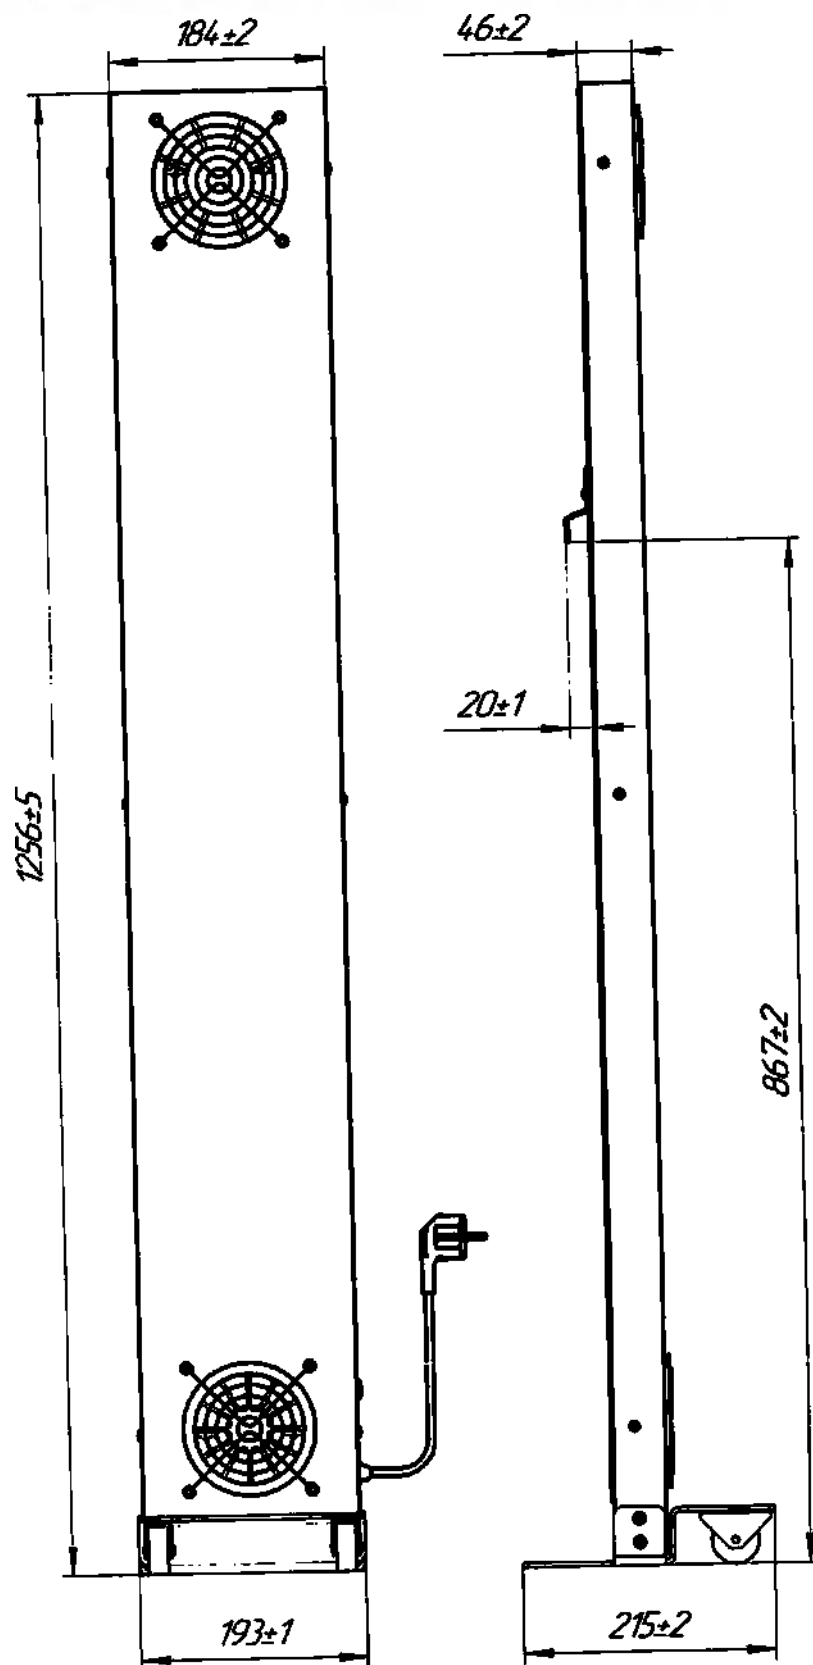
Облучатель РВ-30, РВ-40 и РВ-80 смонтированный на мобильную опору
